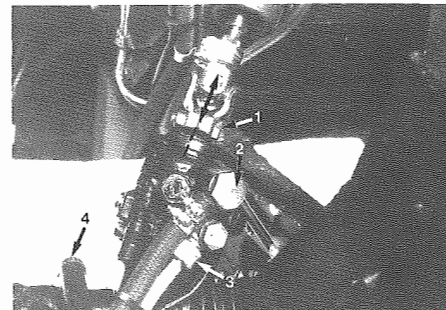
1 - Vite fissaggio fascetta inferiore
